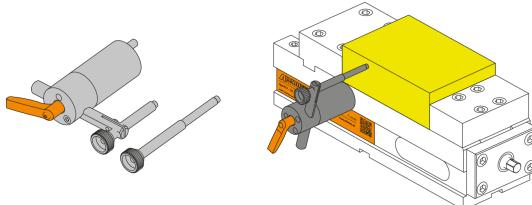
Упор обрабатываемой детали 692 128 5650 144
